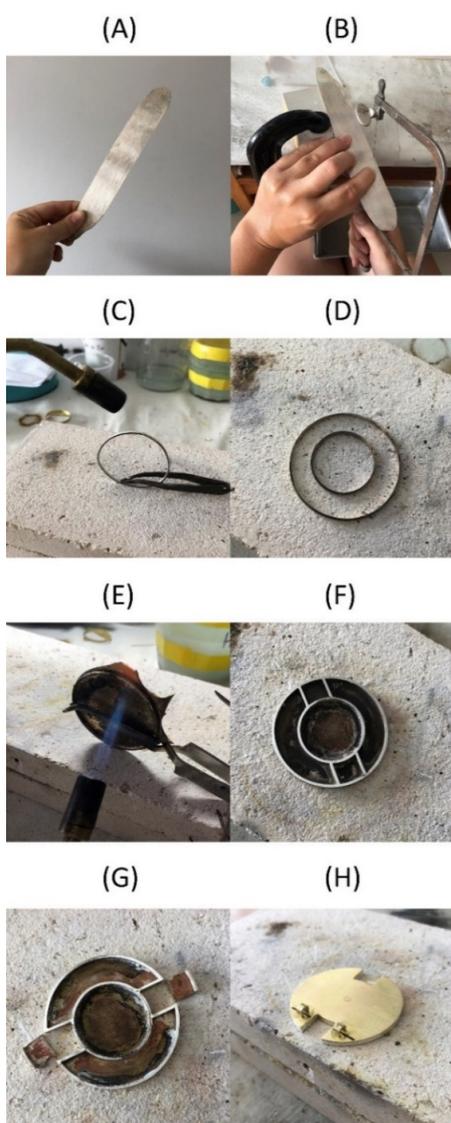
Processo de fabricação da parte metálica: (A) chapa de prata; (B) recortes; (C) e (D) círculos soldados; (E) círculos de prata sendo soldados à chapa; (F) chapas para estrutura; (G) recorte das partes sobressalentes e (H) soldagem das argolas.
